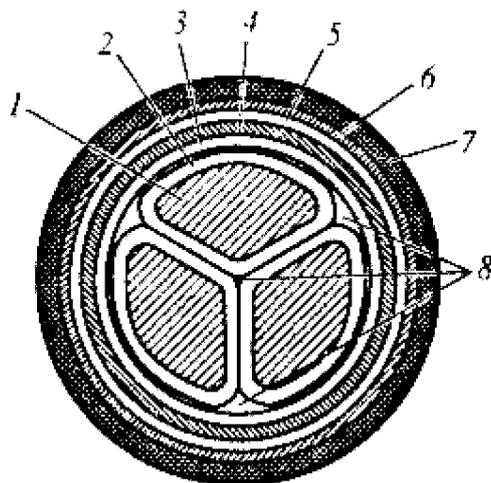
Трехжильный кабель с бумажно-масляной изоляцией на напряжение 10 кВ:
